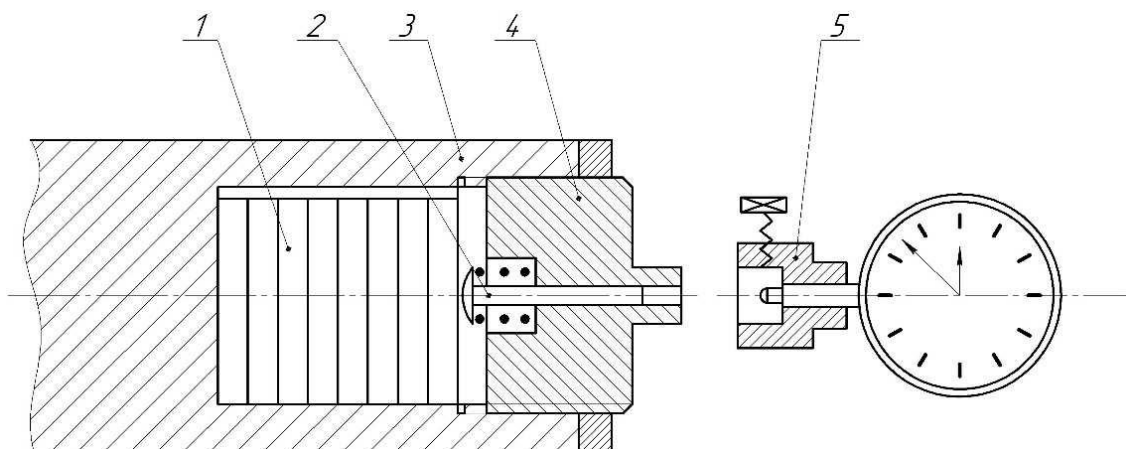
Багатоелементний динамічний гаситель коливань з пристроєм для калібрування осьового зусилля стиснення.
